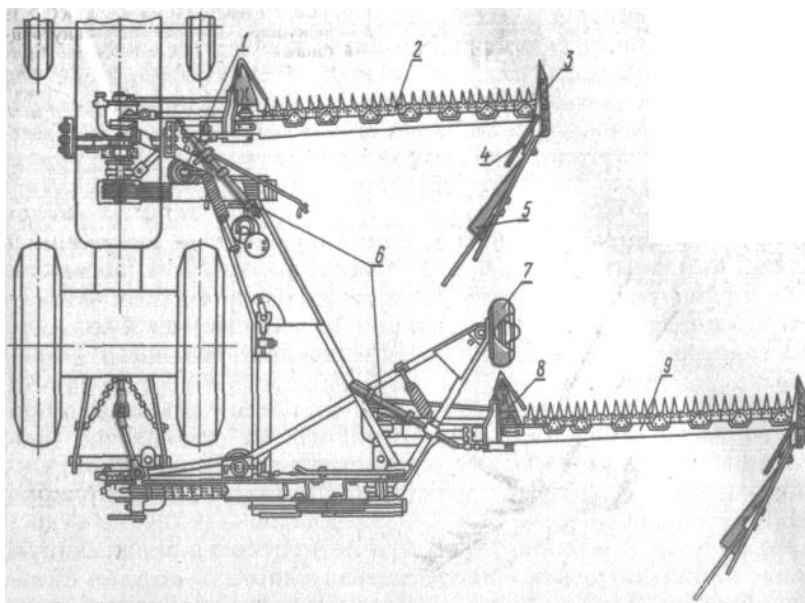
Схема двухбрусной полунавесной косилки КДП-4:
